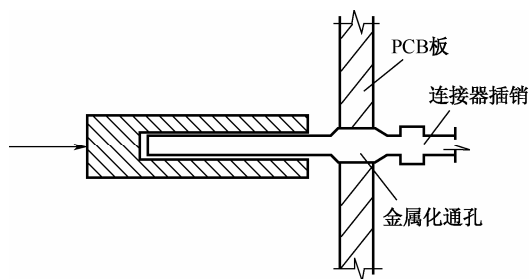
连接器和 PCB 金属化通孔之间的压接接续
